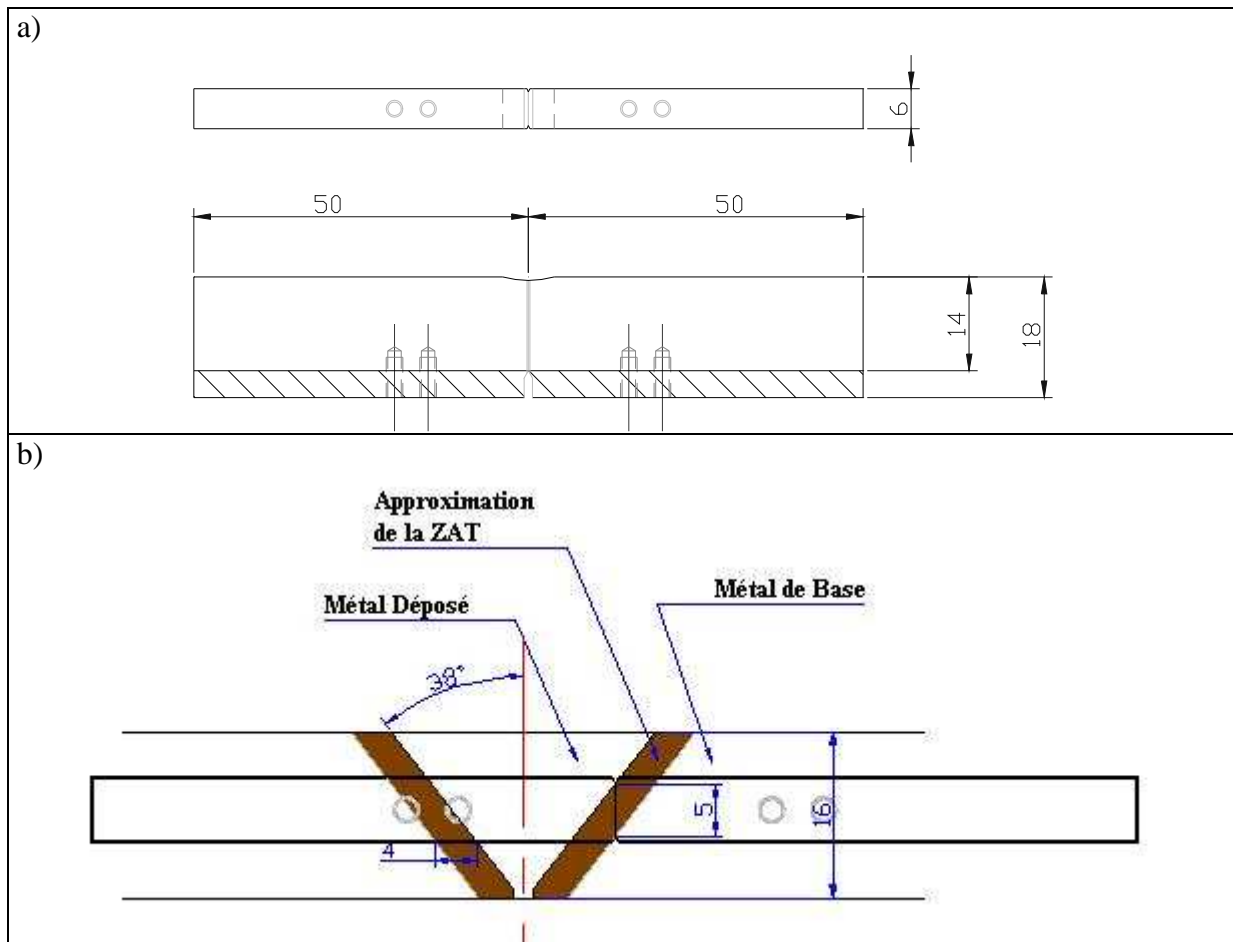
a) Géométrie des éprouvettes SENB d'épaisseur 6 mm (SENB01Ep6)
